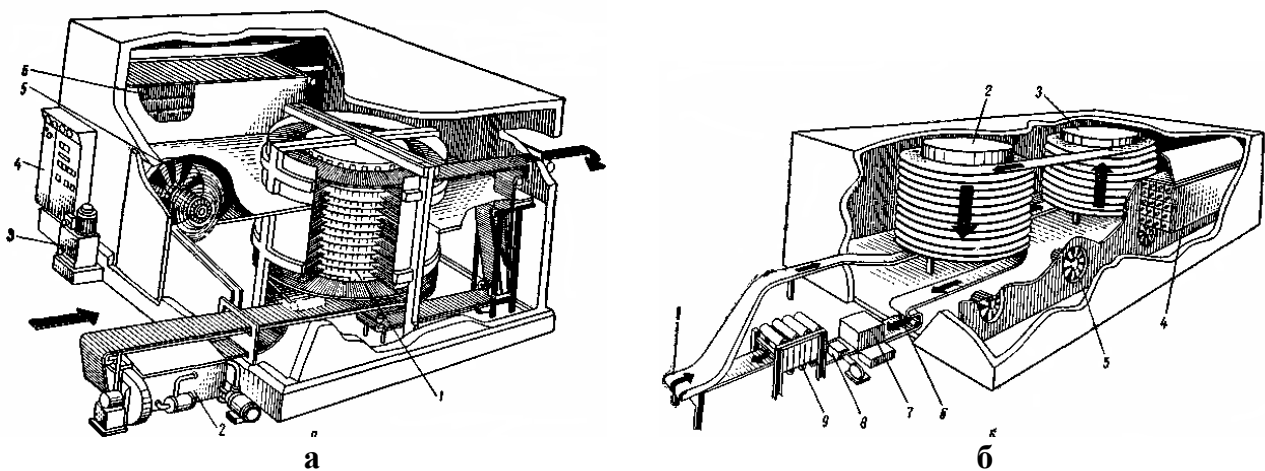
Морозильні апарати «Гірофриз»: а – з одним барабаном: 1 – барабан; 2 – пристрій для миття стрічки; 3 – перетворювач частоти; 4 – розподільний щит; 5 – вентилятор; б – повітроохолоджувач; б – з двома барабанами: 1 – пристрій для перевертання стрічки; 2 – другий барабан; 3 – перший барабан; 4 – повітроохолоджувач; 5 – вентилятор; 6 – вузол розвантаження; 7 – пристрій для миття; 8 – вентилятор сушіння стрічки; 9 – натяжний пристрій
